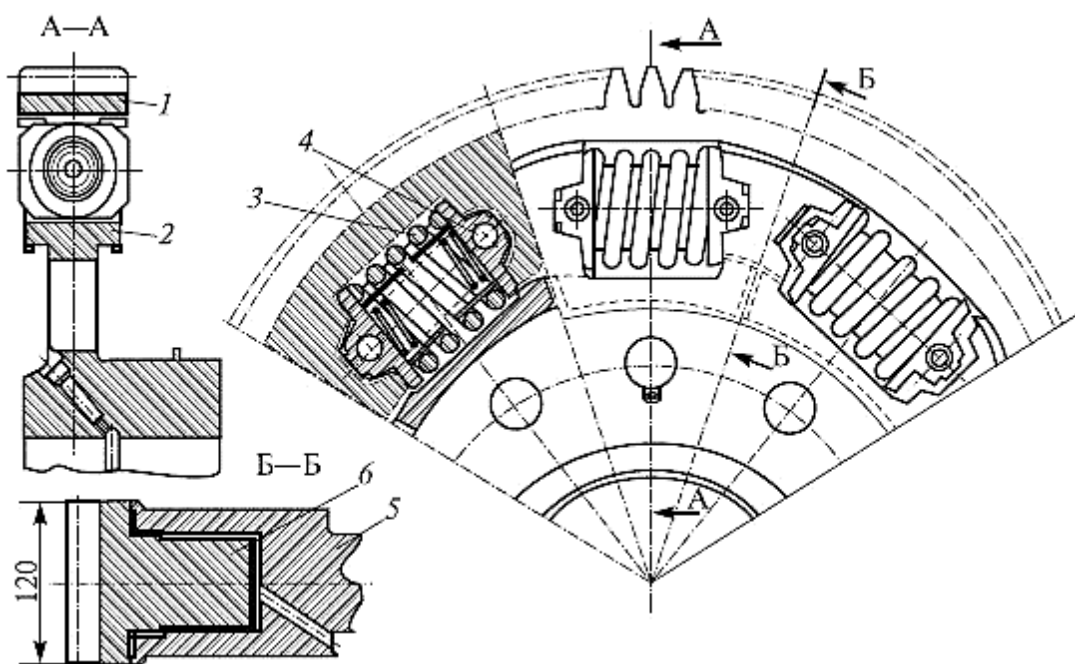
Зубчасте колесо з циліндричними пружинами:
